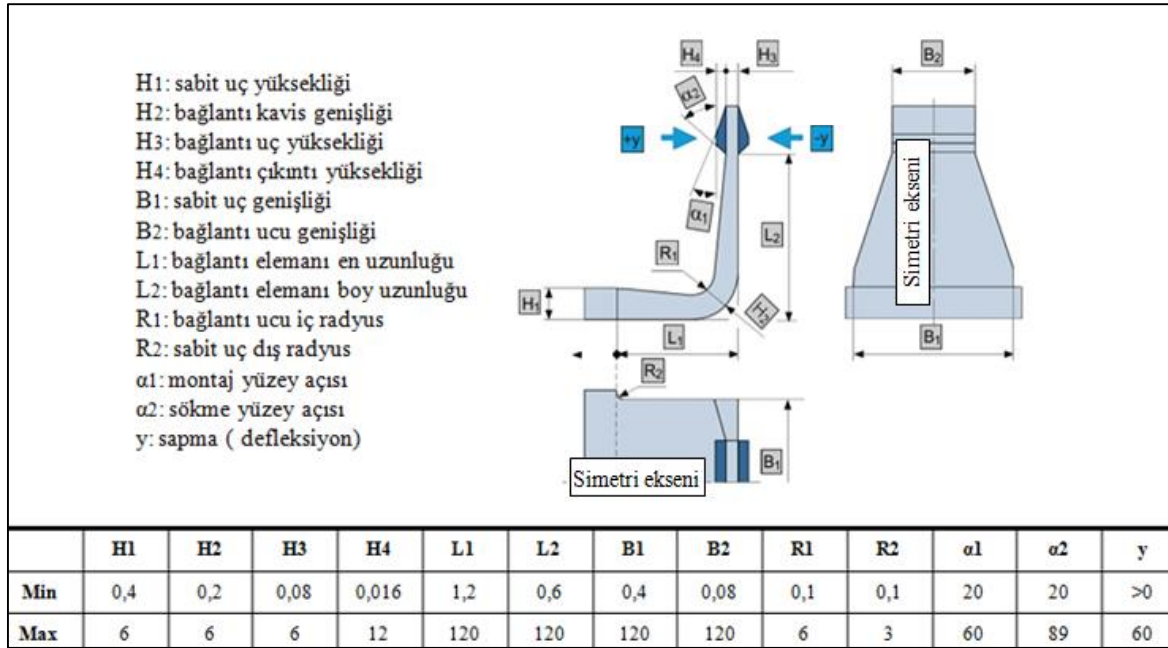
C tipi esneyerek kilitlenen bağlantı elemanının boyutlandırılması [42]
